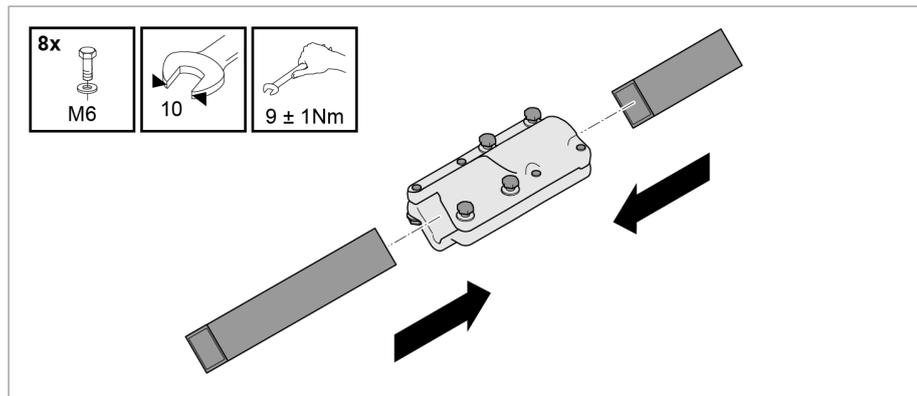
Visser le tube carré et l'isolateur à la pièce d'accouplement double
